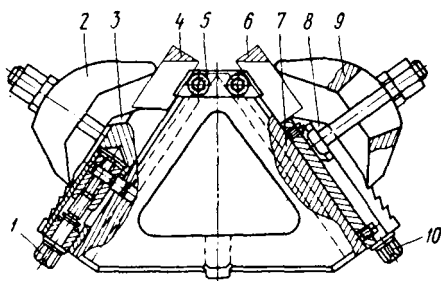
Универсально-наладочное приспособление для обработки клиньев
